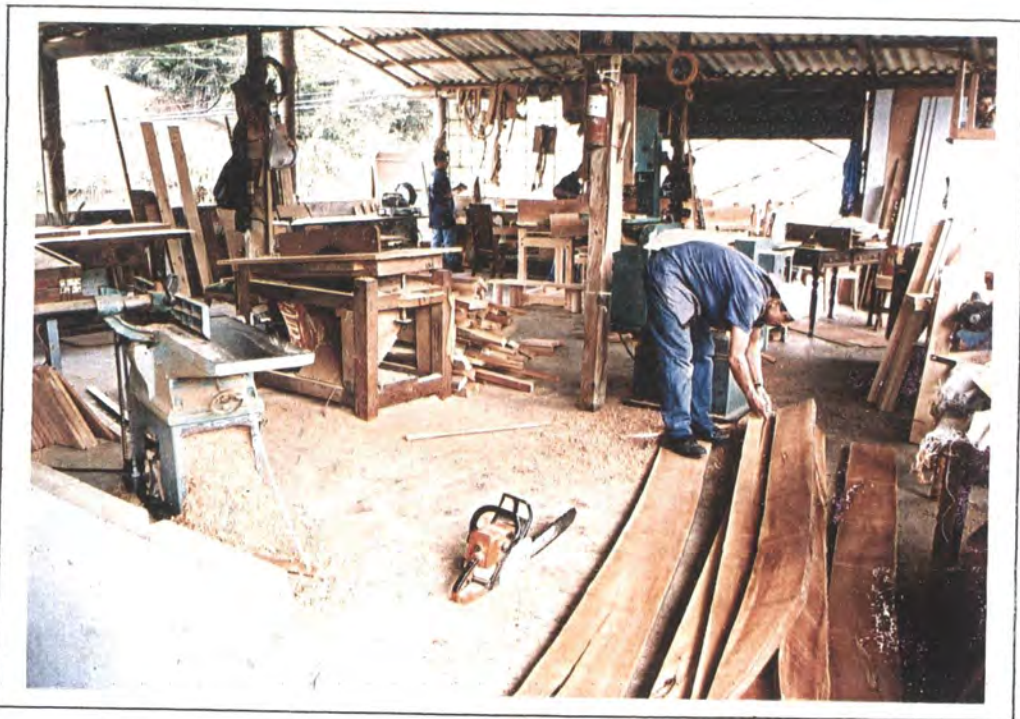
CORTE Y ENSAMBLE / MUEBLES NAZARETH
